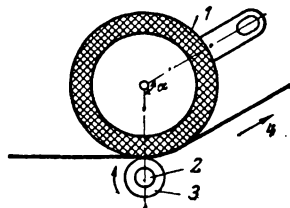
Узел ведущего вала. 1 — обрезиненный прижимной ролик; 2 — вал двигателя; 3 — насадка; 4 — лента.
